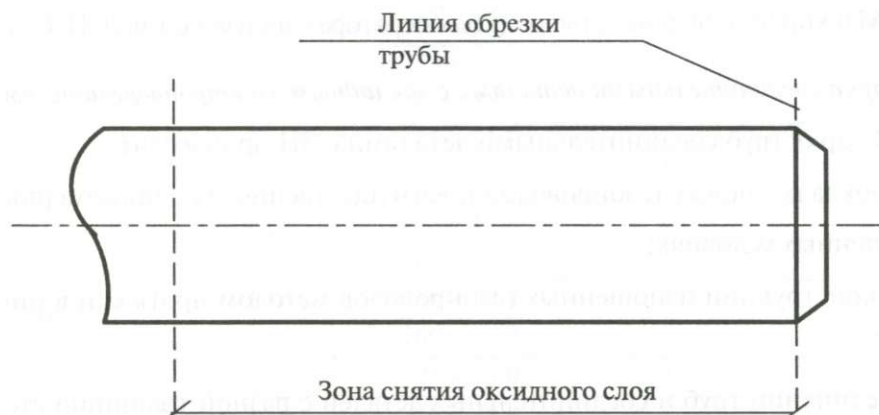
Подготовка конца трубы к сварке
